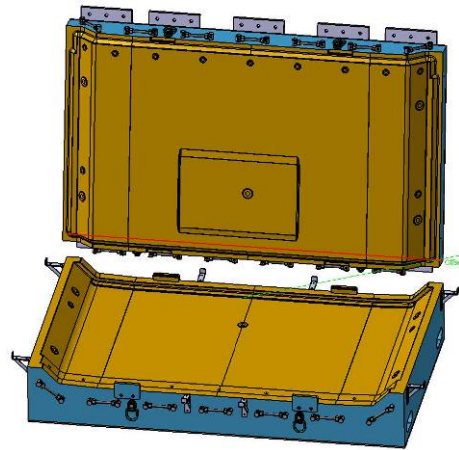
Werkzeug Bodenplatte 2 (CAD)
